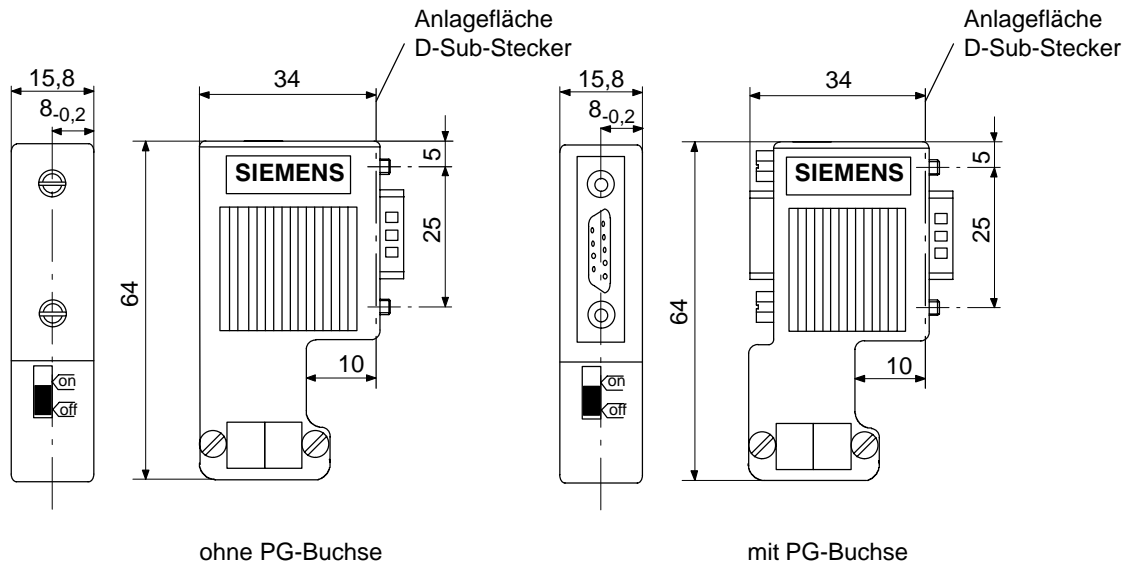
Busanschlußstecker in IP 20 (6ES7 972-0B.11-0XA0)
